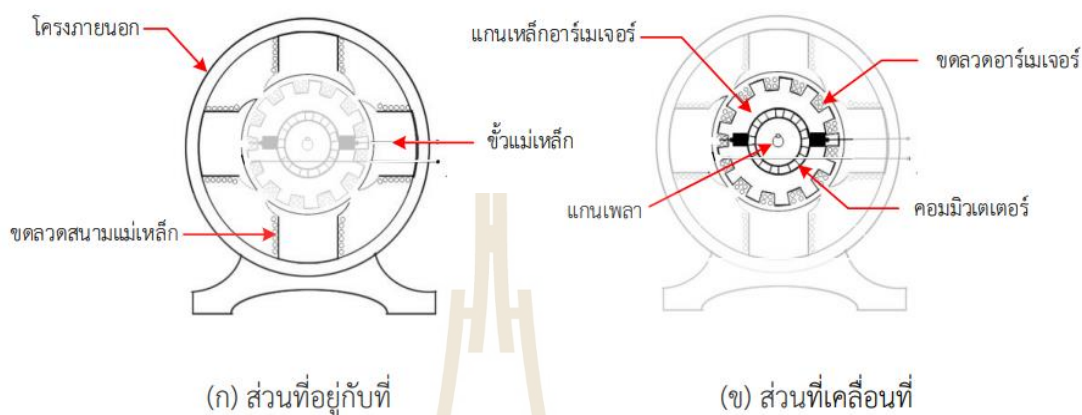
ซิงโครนัสมอเตอร์
